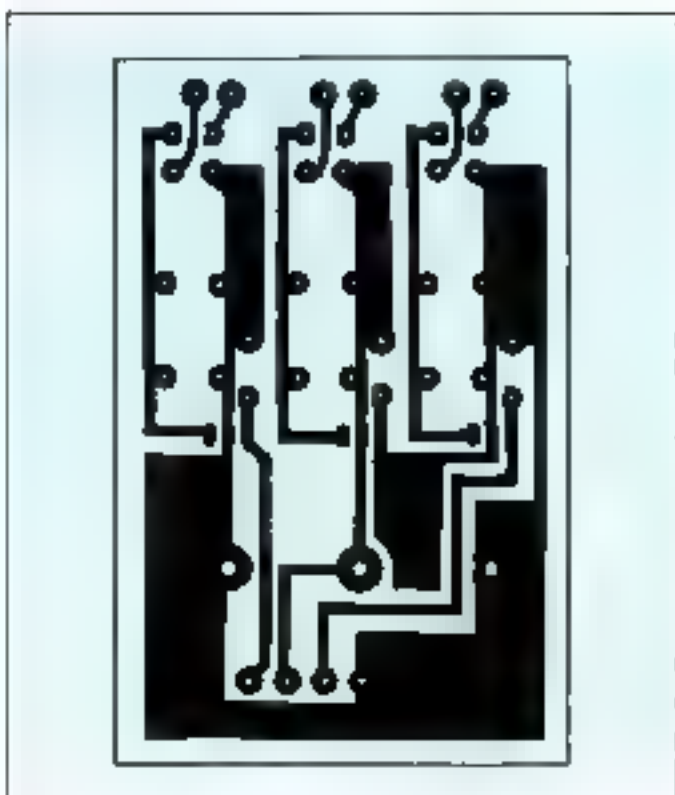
Circuit imprimé de l'alimentation vu côté soudures.
